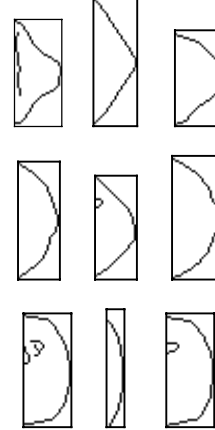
Örnek bir kesici takım imgesi ve kenarları
